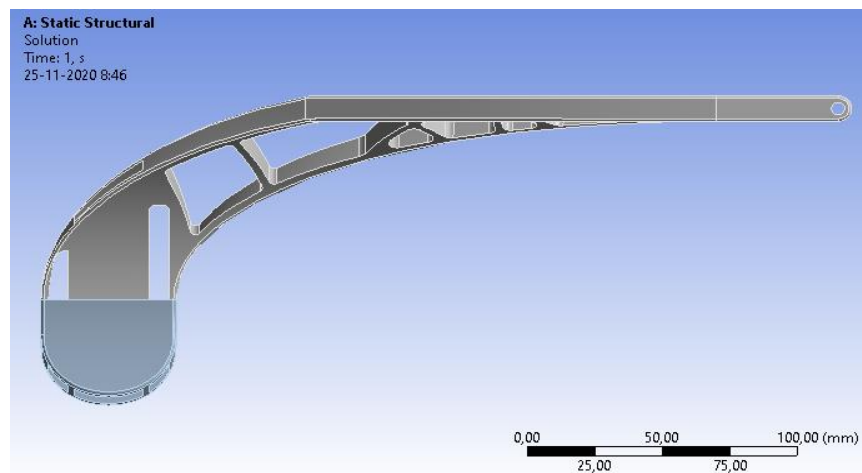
Vista 2 rediseño N°1 de eslabón pierna izquierda.
